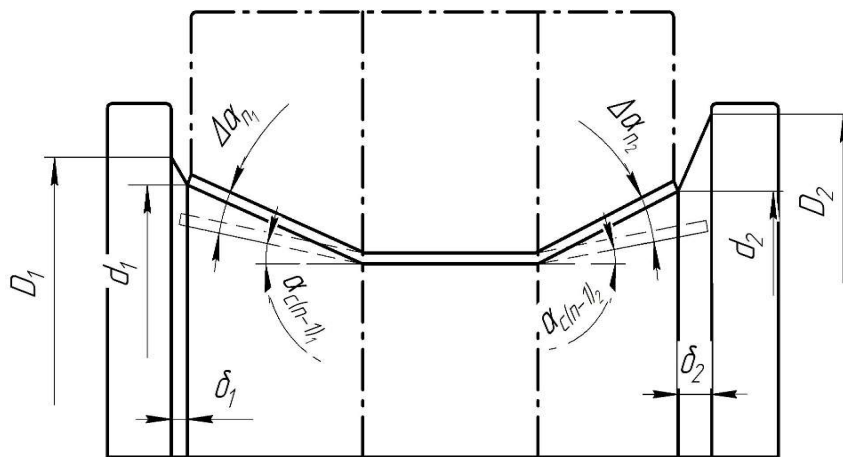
Схема вала с дополнительными переходными конусными участками
